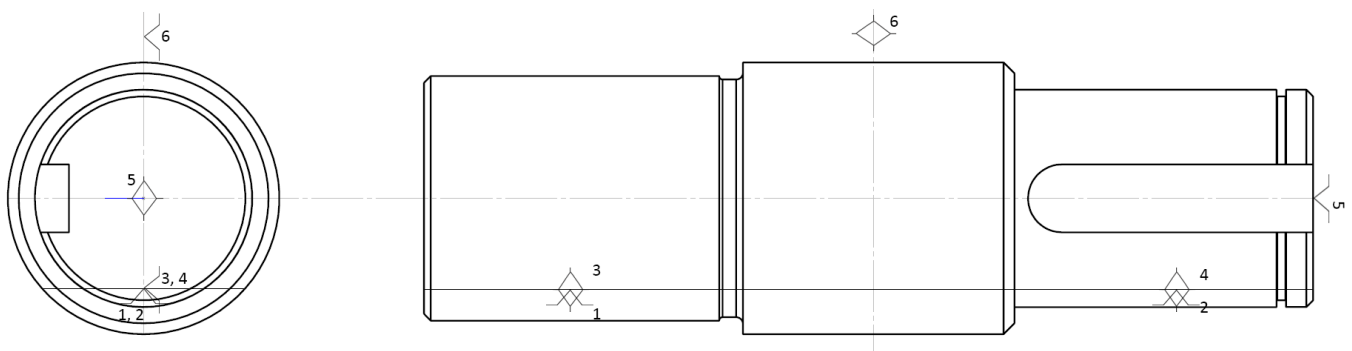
Схема базування оброблюваної поверхні 12.
